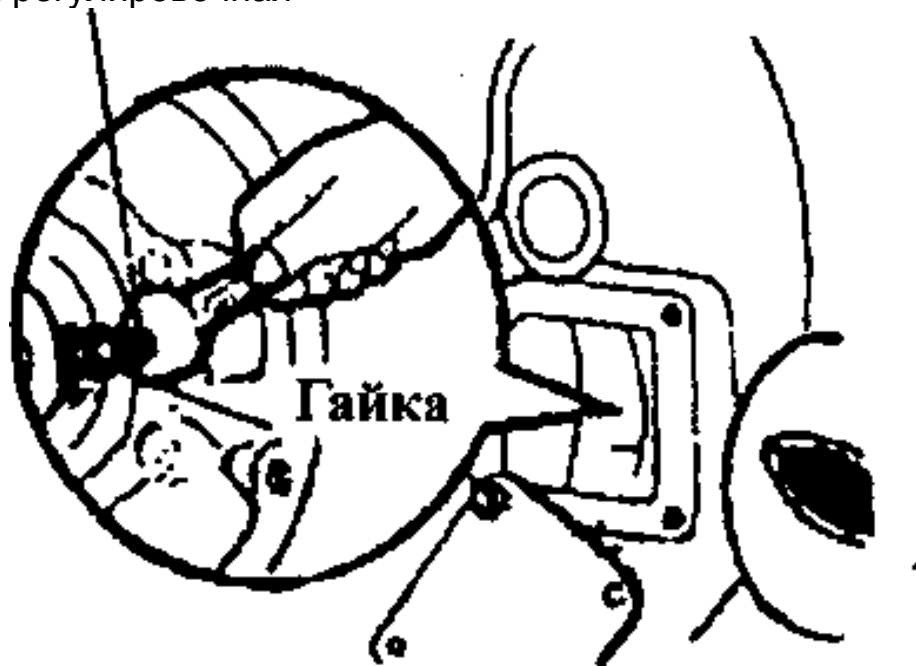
Регулировка зазора между отжимным кольцом и выжимным подшипником
